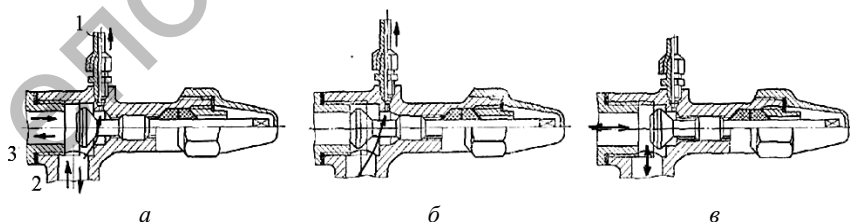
Работа запорного трехходового вентиля компрессора:
